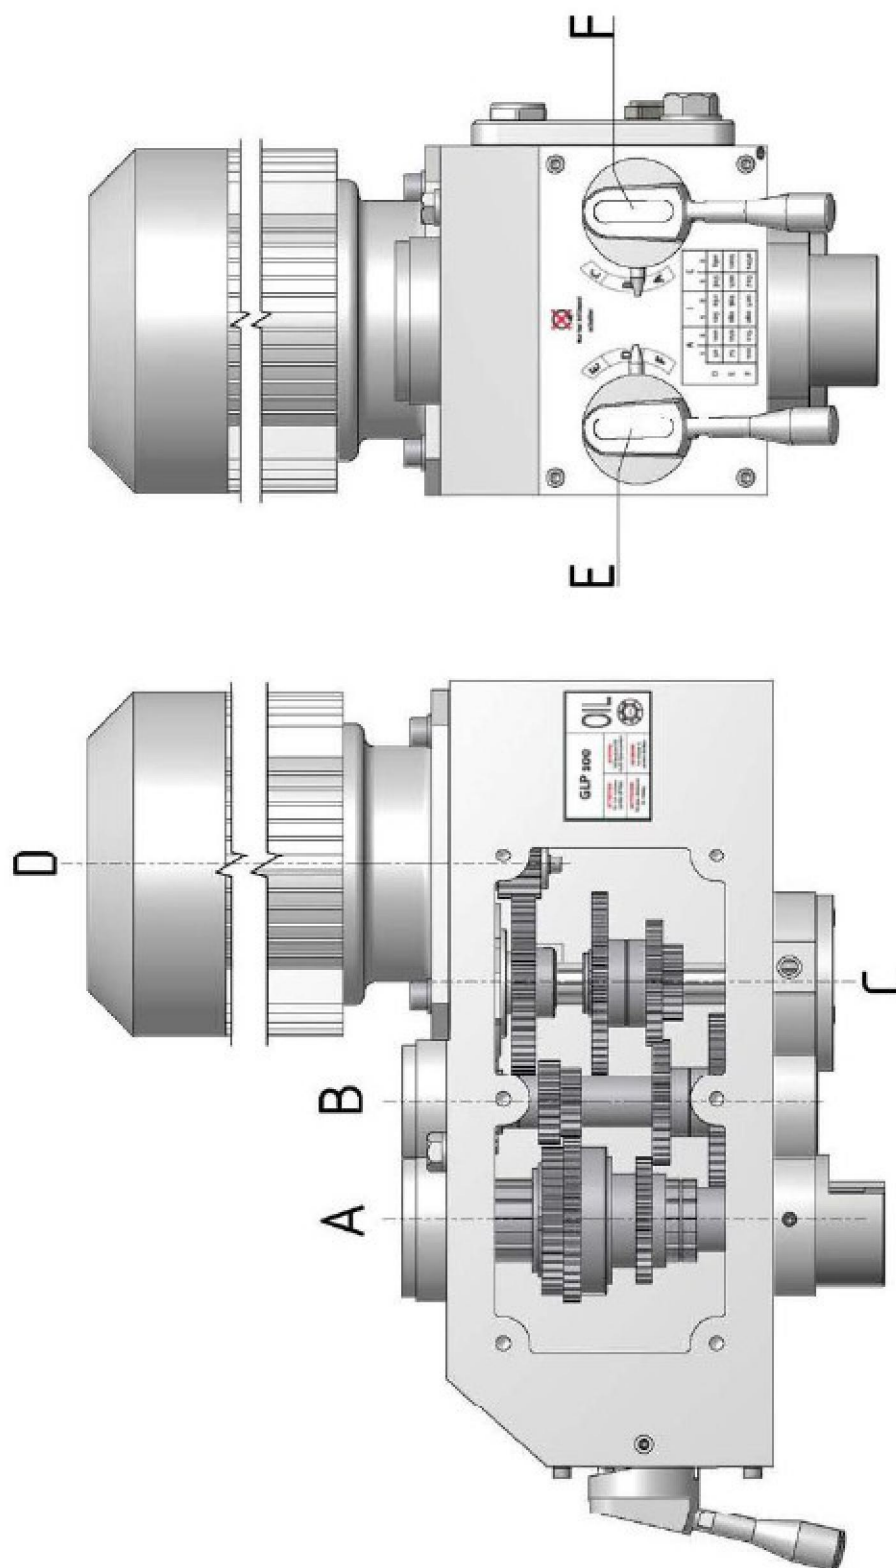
Husillo principal caja de engranajes - Gear box main spindle
